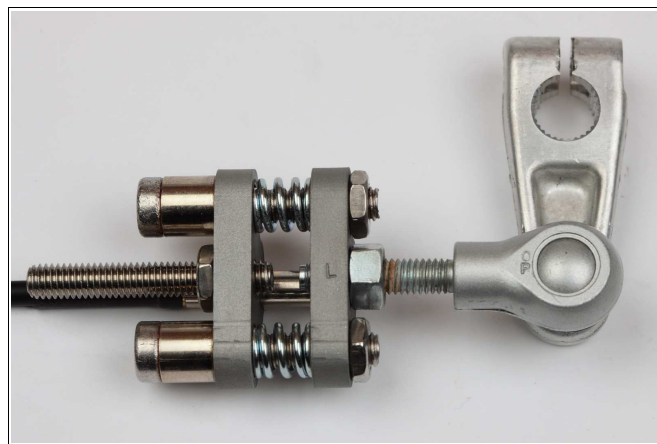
Magnetplatte mit M6-Linksgewinde.
